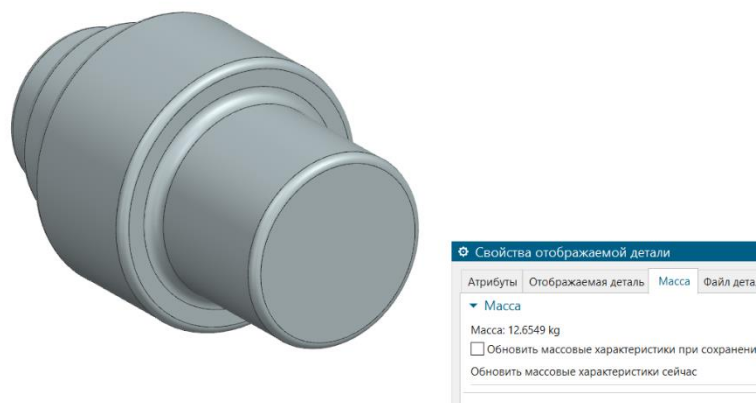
3Д-модель заготовки отриманої на пресі
